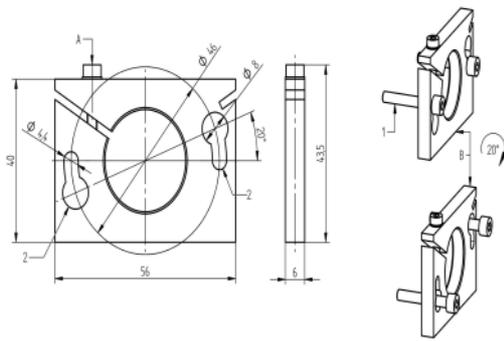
Support pour FS60 pour FFS08, FFS06 (imprimé n° DLT7660)
